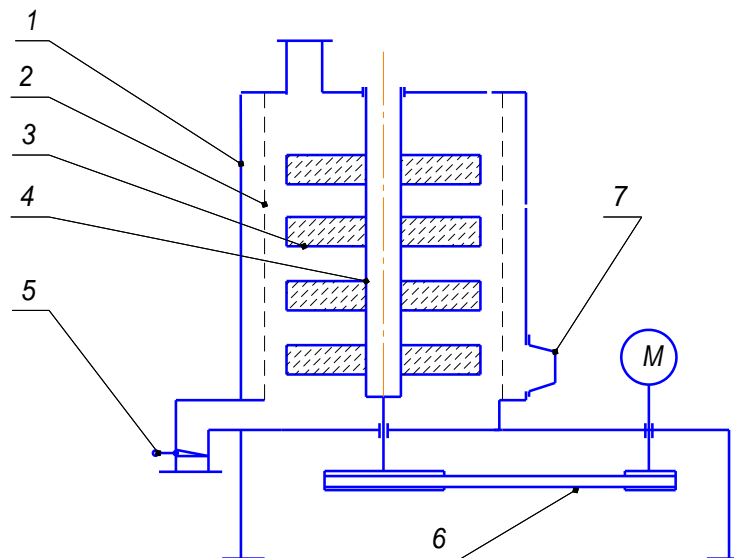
Машина для луцення та шліфування зерна: 1-корпус; 2-сітка; 3-диск; 4-вал; 5-регулятор; 6-привід; 7-патрубок повітряний
